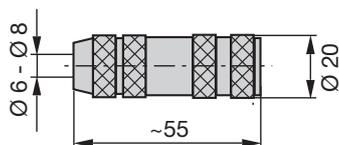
Connecteur BKS-S103-00 (douille) pour BUS IN
